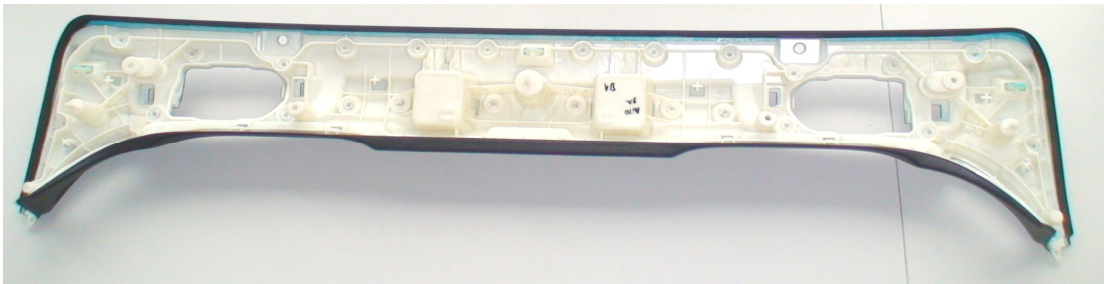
Conjunto 'Rückwand' (lado técnico)
